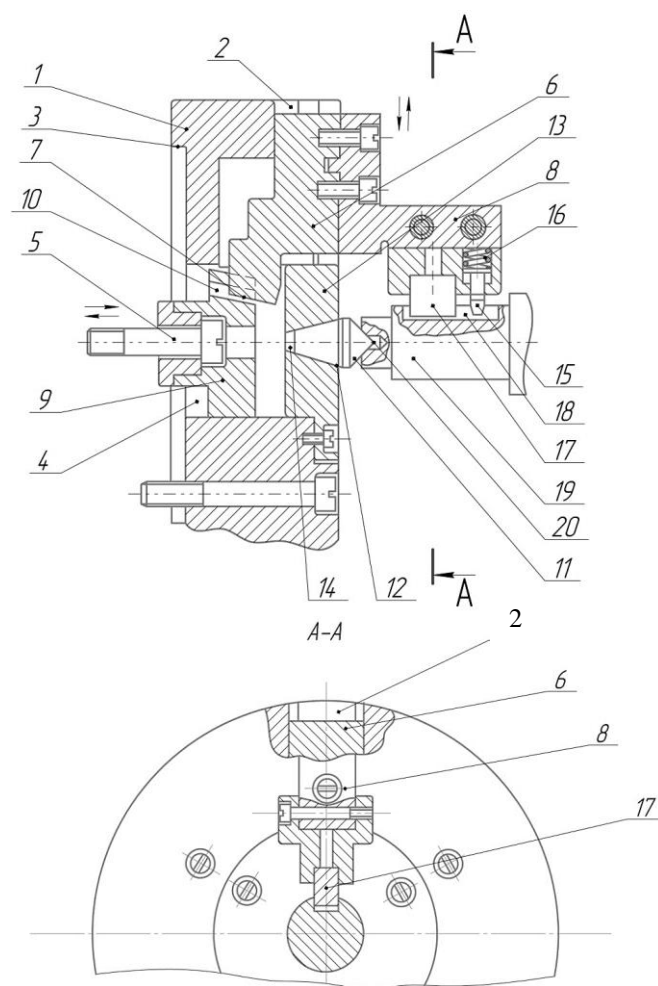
Патрон кулачковый клиновой механизированный для установки вала со шпоночным пазом на центрах станка
